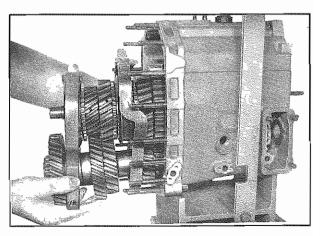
Insertmento dell'albero primario e secondario Inserting the main shaft and countershaft
